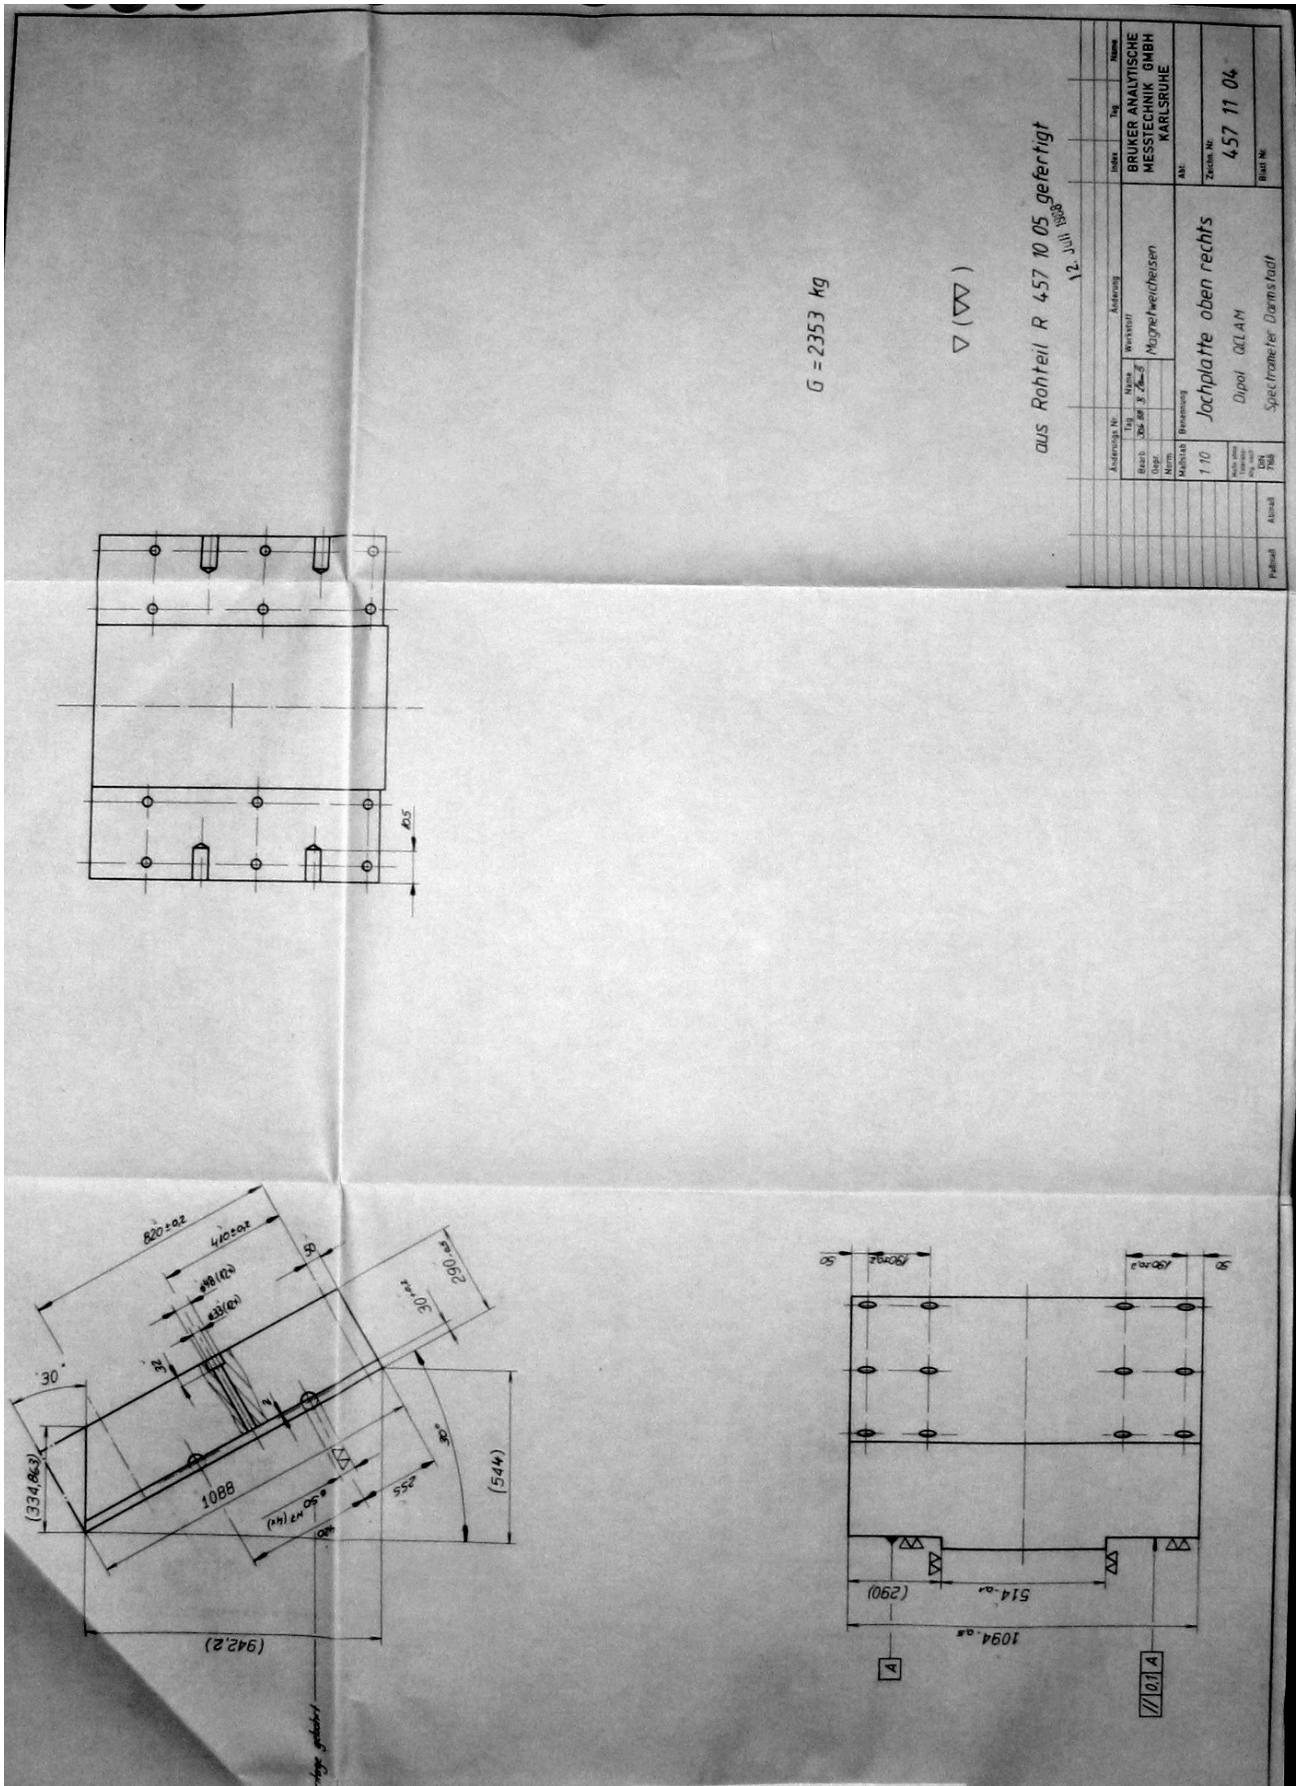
Technische Zeichnung der rechten oberen Jochplatte des QClams.
